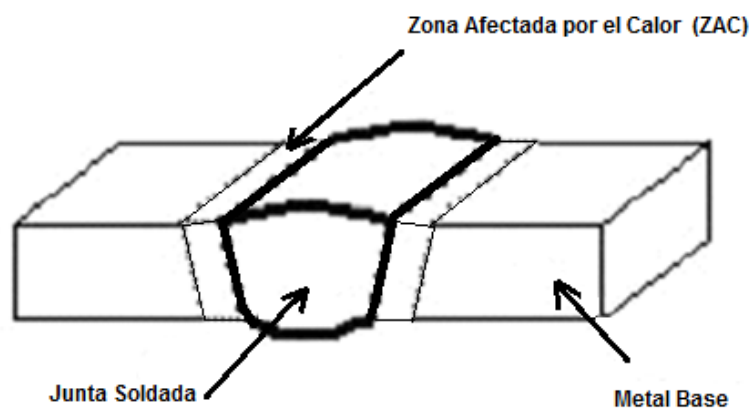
ESQUEMA DE UNÓN SOLDADA
